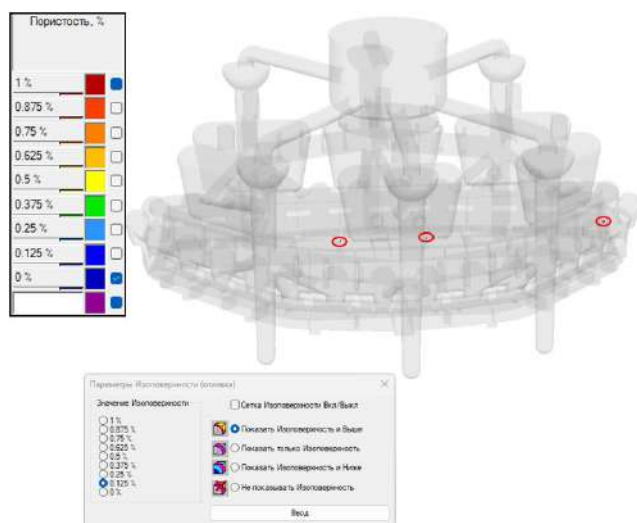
Отливка детали «Корпус с фланцами» с оптимизированной конструкцией ЛПС.
